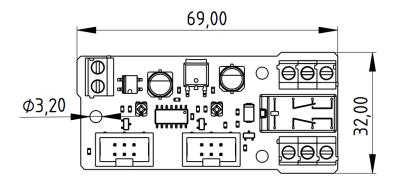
Dimensions du module (toutes les côtes sont données en mm).
